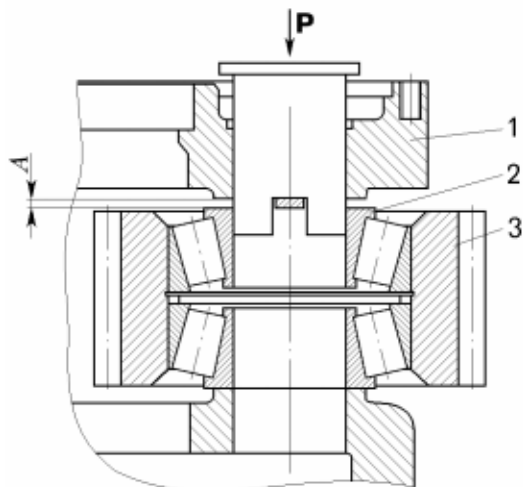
Регулировка подшипников сателлитов второго ряда:
